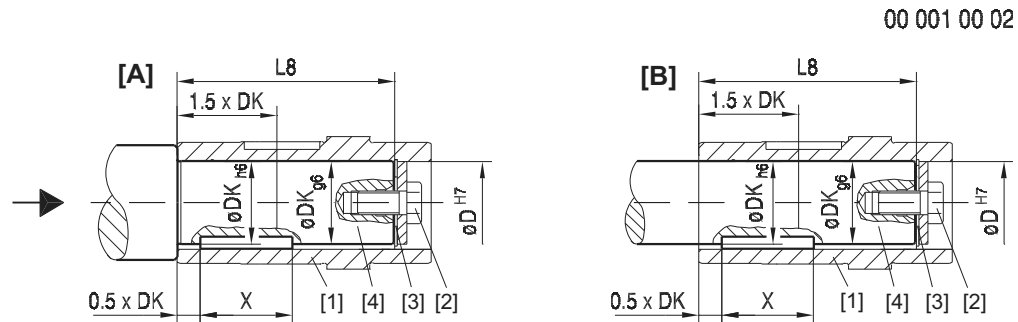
Eje de la máquina con tope (A) y sin tope (B)
